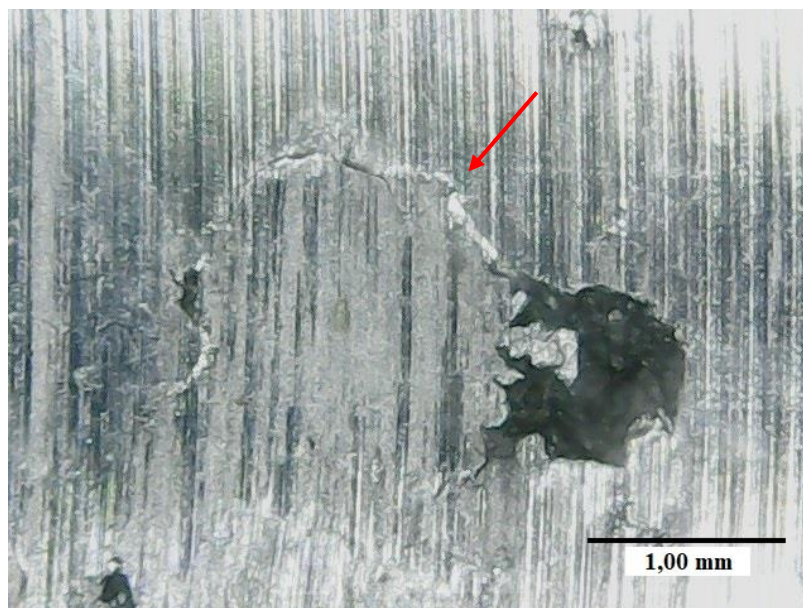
Detalhe de inclusão arredondada com ligação direta a uma fissura linha
